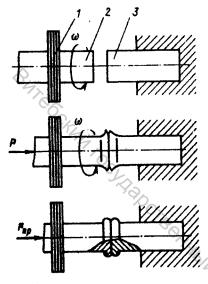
Схема инерционной сварки: 1 – маховик: 2. 3 – свариваемые заготовки
